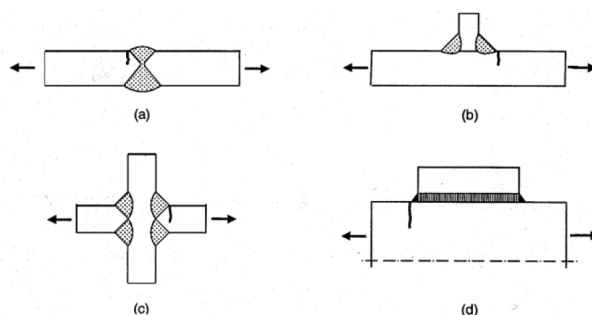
Rotura no pé da soldadura, adaptado de [21]
